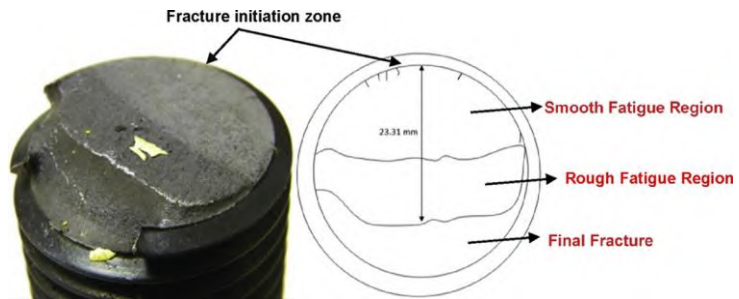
(a) Penampang material baut patah (b) penampang baut patah dengan pembesaran [5]
